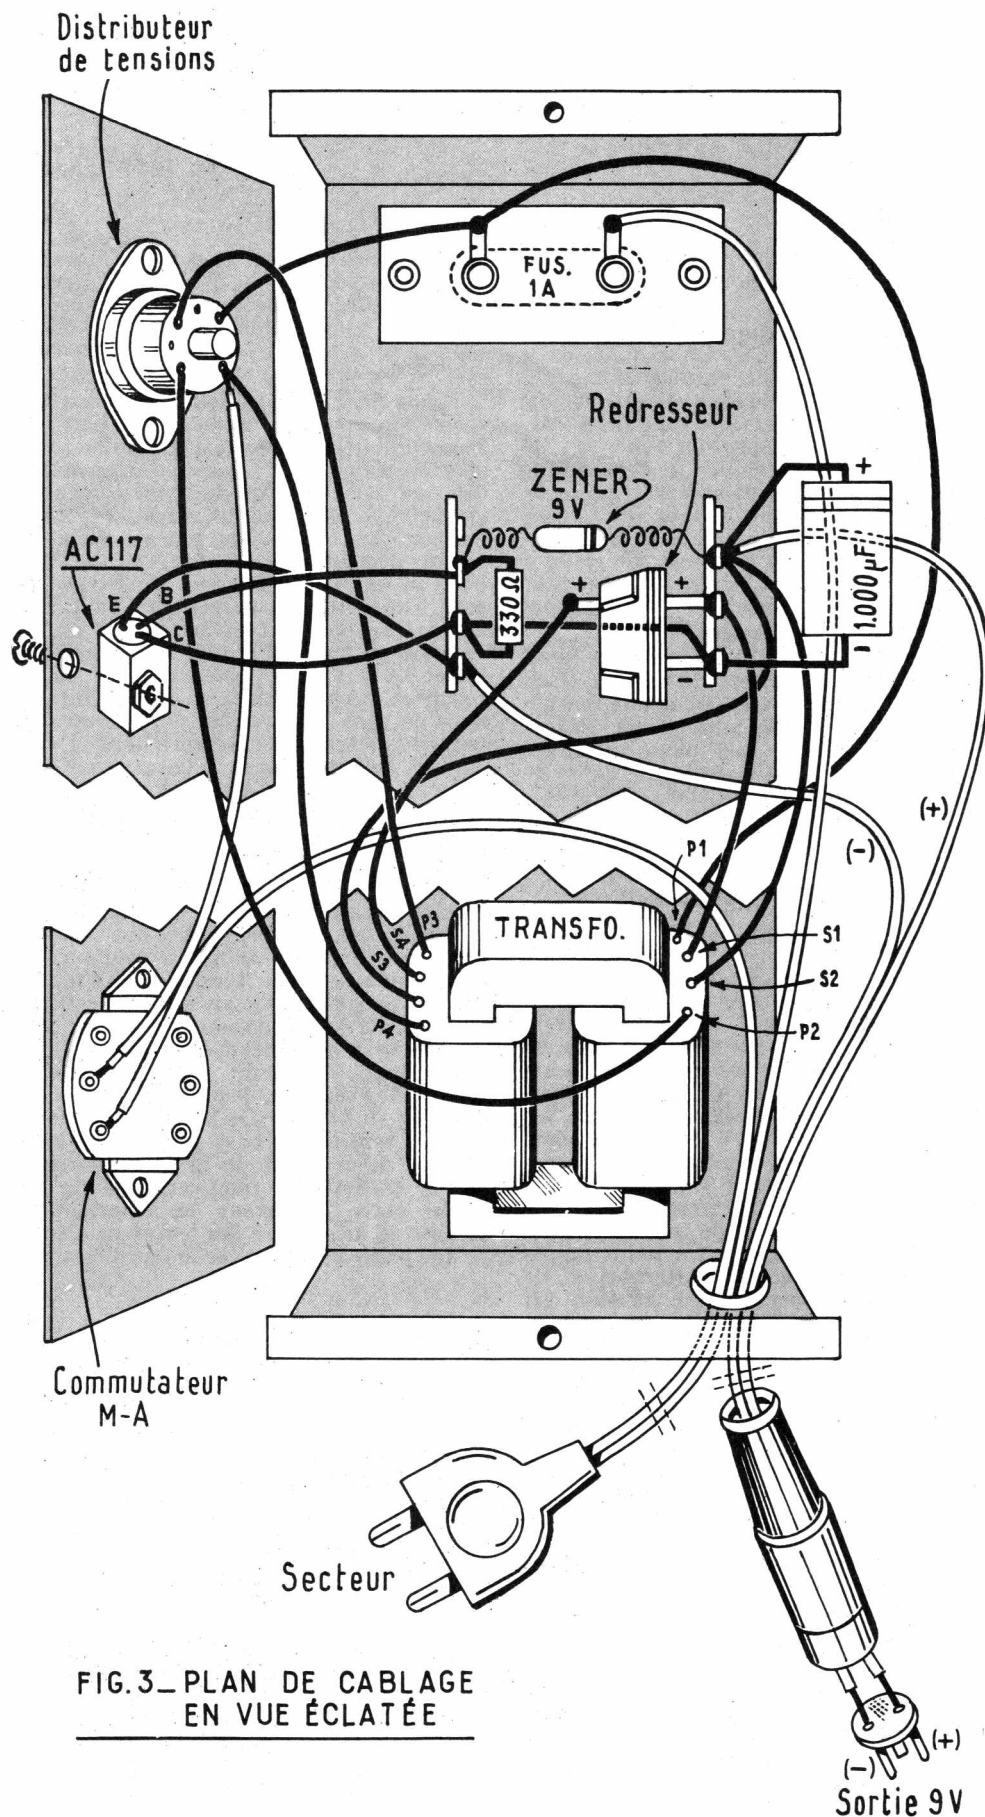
PLAN DE CABLAGE EN VUE ÉCLATÉE
